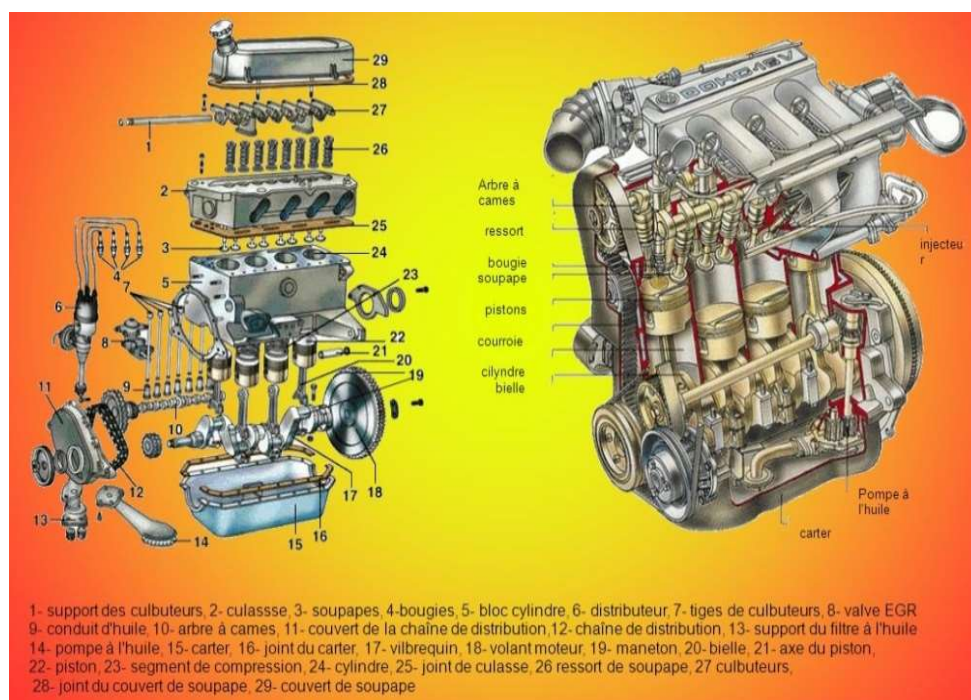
Vue éclatée et assemblée d'un moteur à explosion [3]
